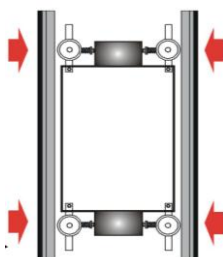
Desenho esquemático da suspensão de elevadores (fonte: Hitachi, Ltd. – Mito Building System Division).
